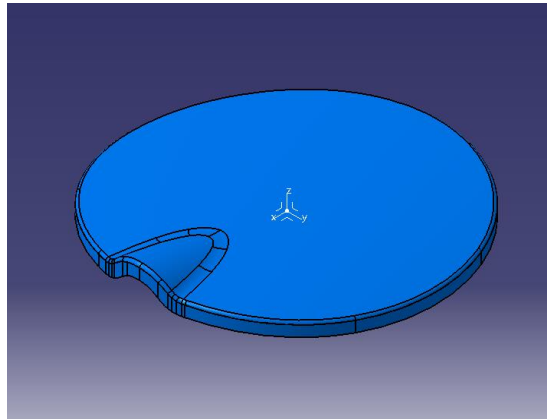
Imagem 3D do produto definido para o projeto da ferramenta de estampagem deste trabalho: *Tampa de Tanque de Combustível*.
